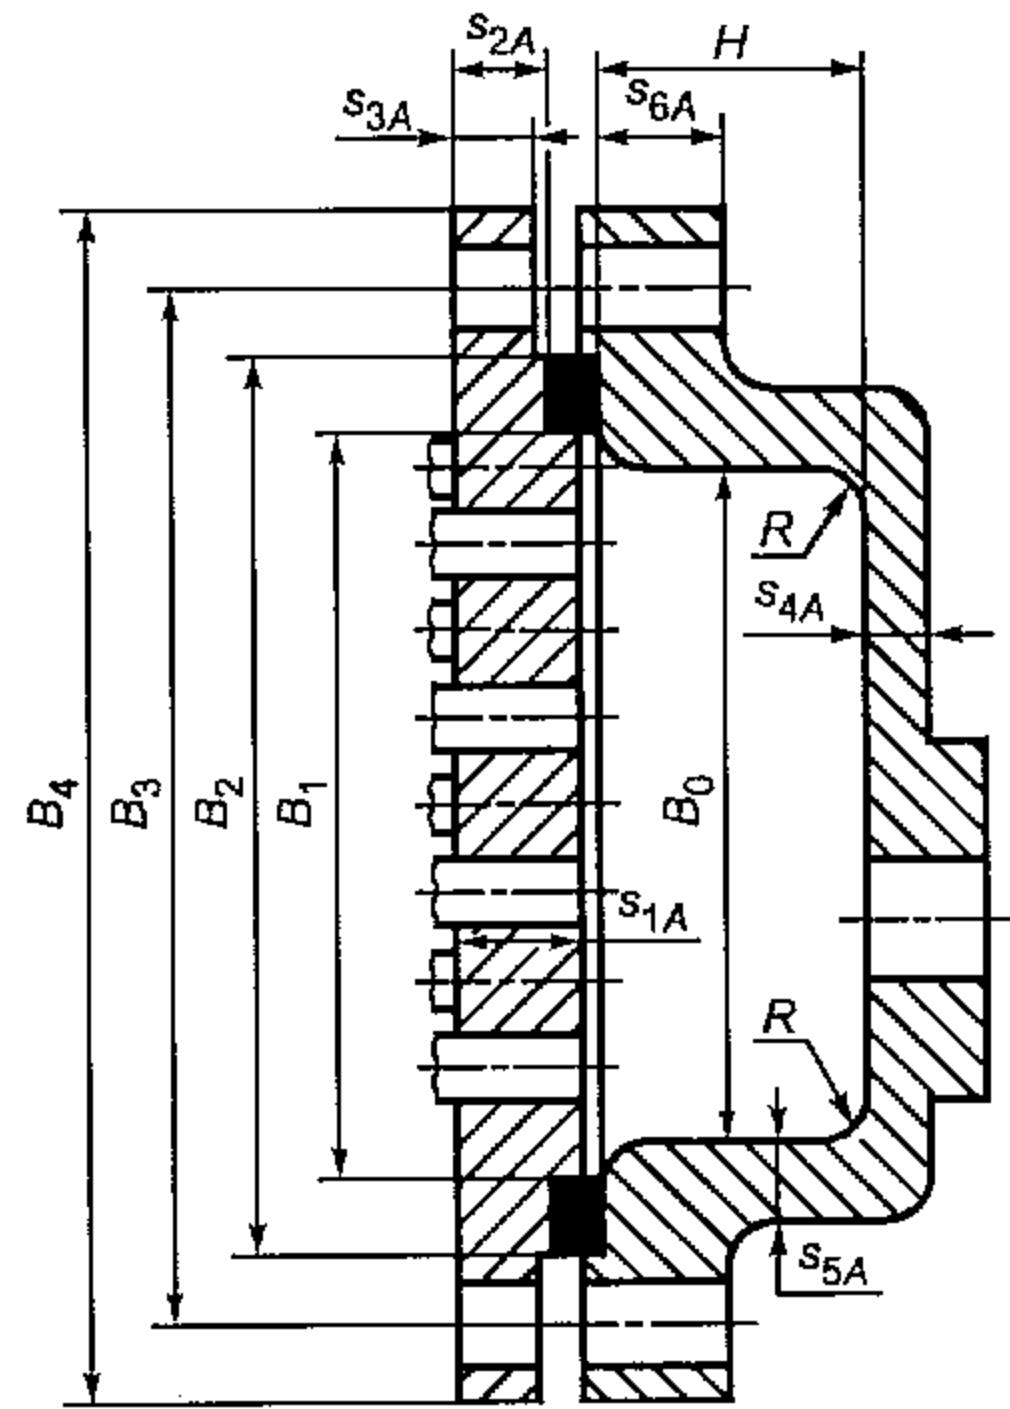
Камера разъемной конструкции с литой крышкой
